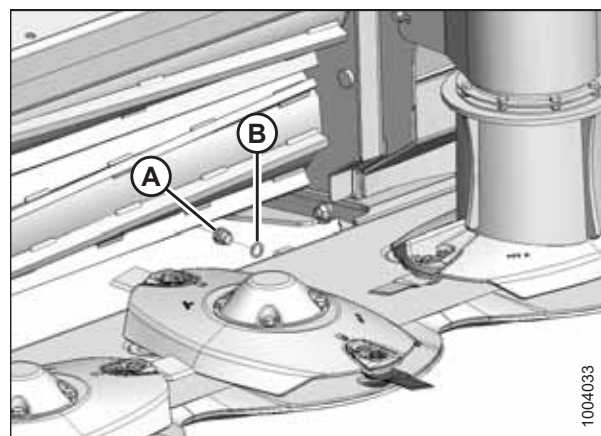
Bouchon d'inspection d'huile de barre de coupe
